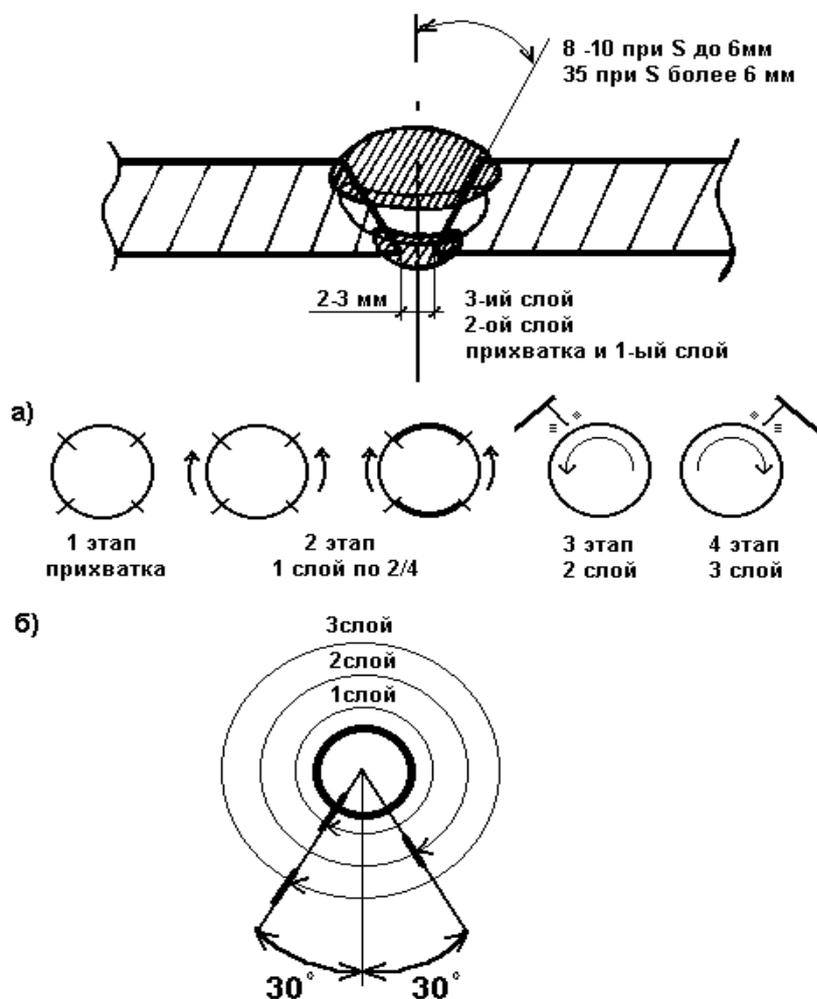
Порядок сварки стыков а, б – соответственно, поворотных и неповоротных стыков.
